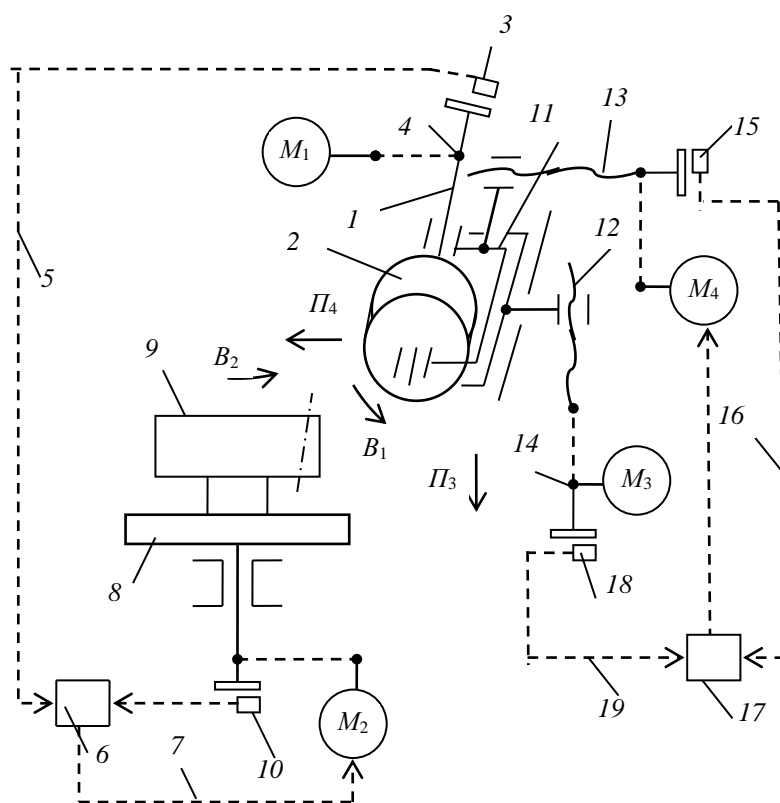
Структура зубофрезерного станка с ЧПУ для обработки колес с наклонными зубьями
